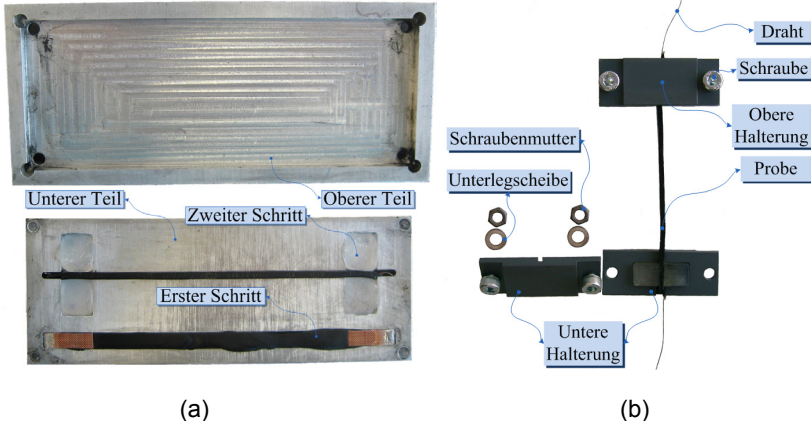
a) Presswerkzeug, b) Halterung mit Probe
